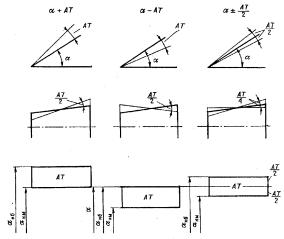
Расположение допуска на угловые размеры относительно номинального значения угла:  $\alpha$  - номинальный угол
